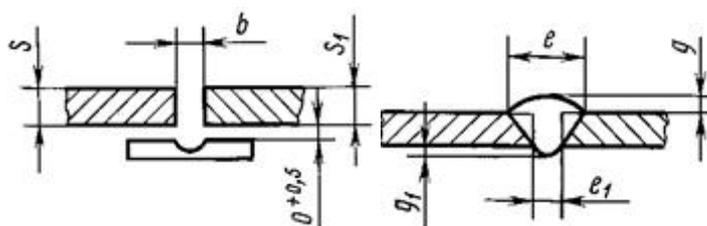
Типы сварного соединения С4 ГОСТ 14771 – 76
